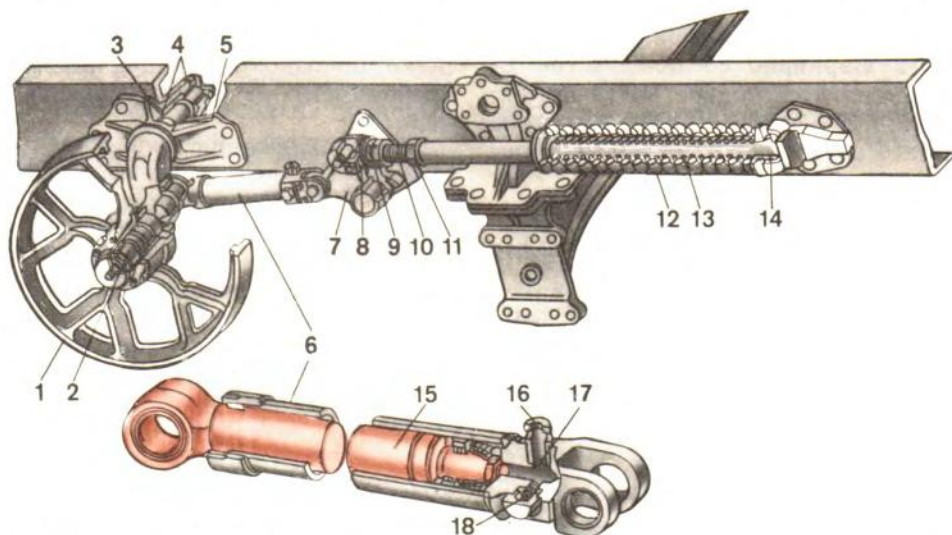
Направляющее колесо с натяжным приспособлением и амортизирующим устройством трактора Т-150:
